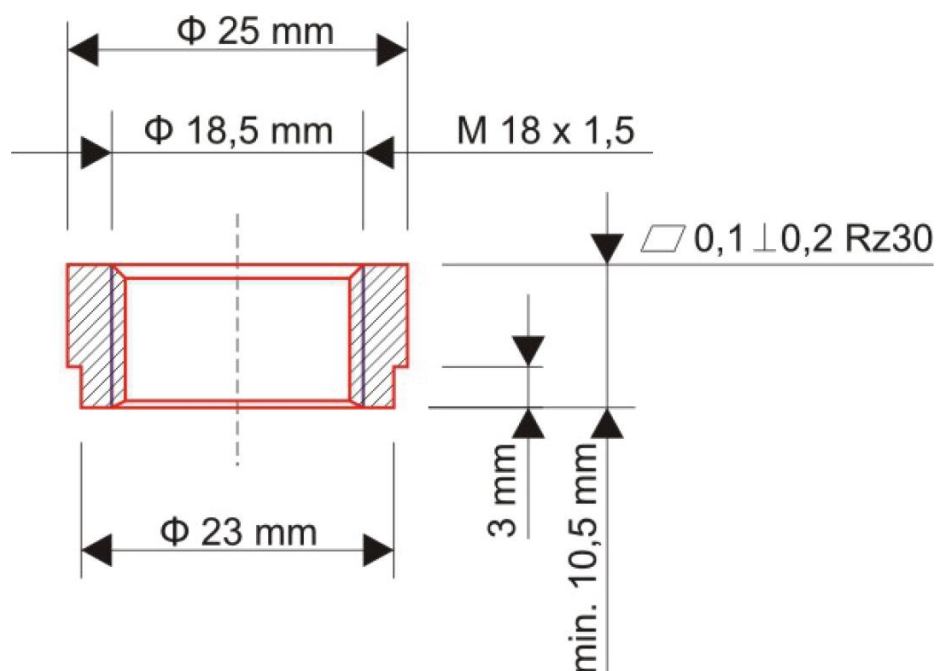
Dimensiones recomendadas del casquillo de montaje de la sonda lambda.
